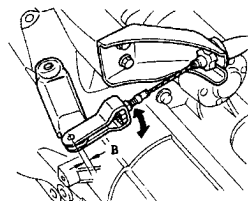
Регулировка свободного хода рычага привода выключения сцепления (См. Раздел 3) В Свободный ход
